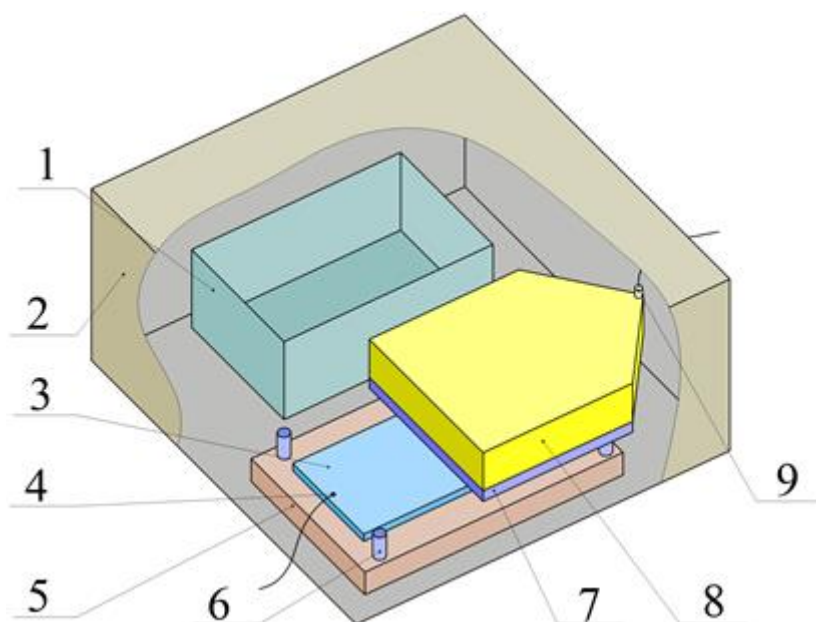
Схема сварки с охлаждением неподвижной пластины (метаемая пластина и заряд условно рассечены): 1 – ёмкость с жидким азотом; 2 – закрытый контейнер; 3 – неподвижная пластина; 4 – термопара; 5 – основание; 6 – сварочный зазор; 7 – метаемая пластина; 8 – заряд ВВ; 9 – детонатор
